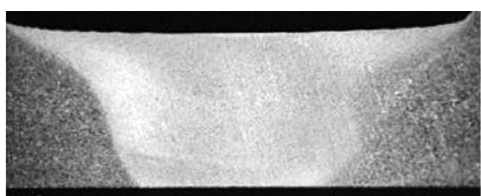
Зоны режимов перемешивающей сварки:
